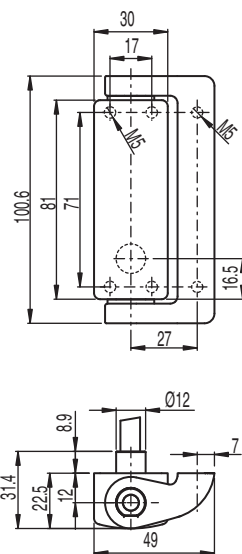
Dimensiones S400-M4-CB2PUR-W en mm
